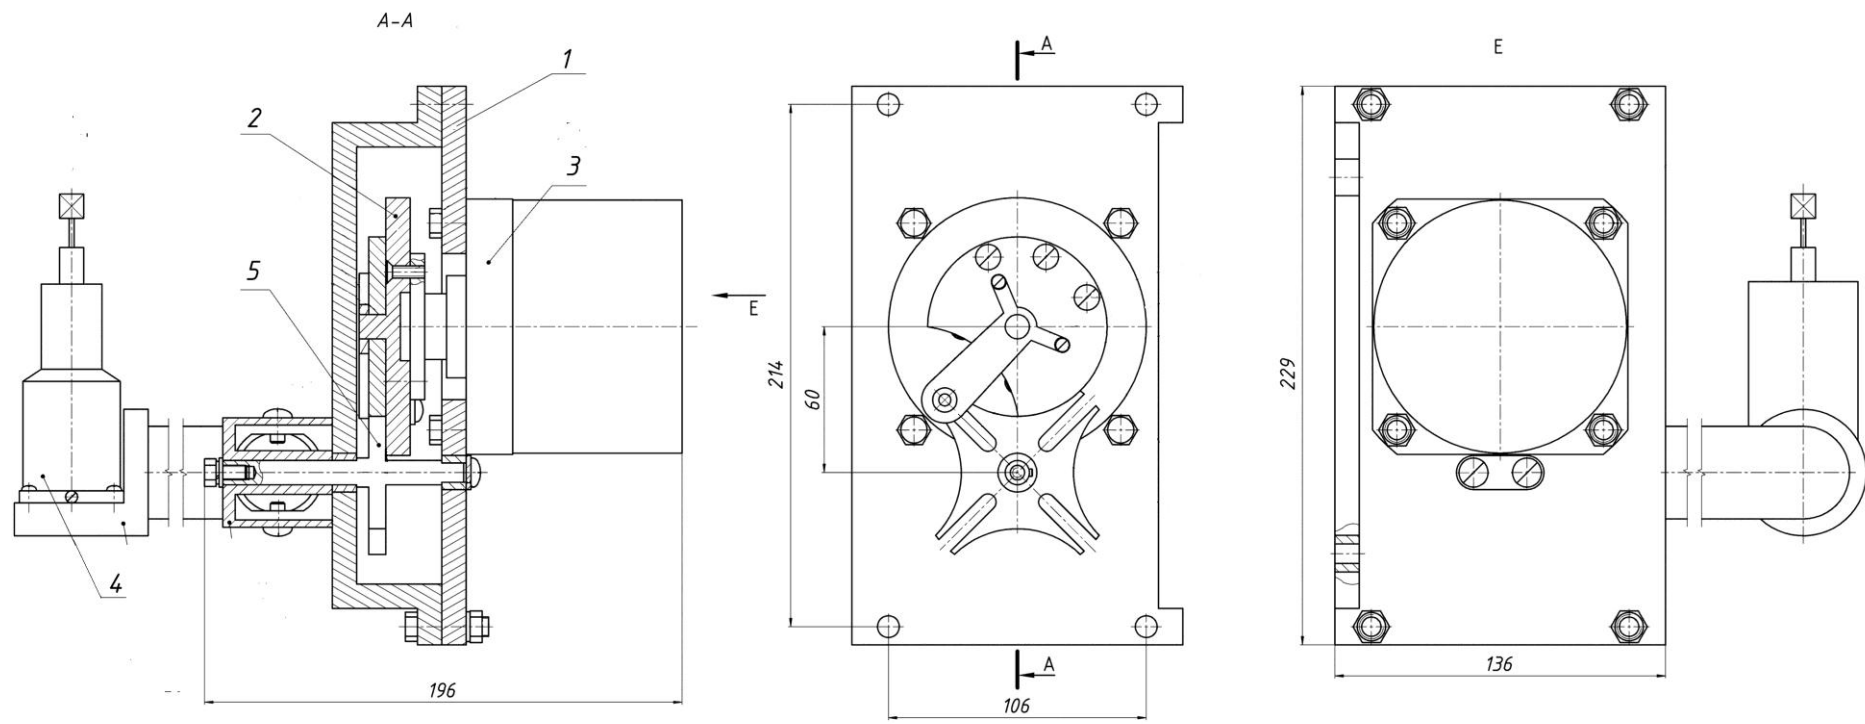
Общий вид автоматического устройства наладки и контроля износа режущих инструментов
